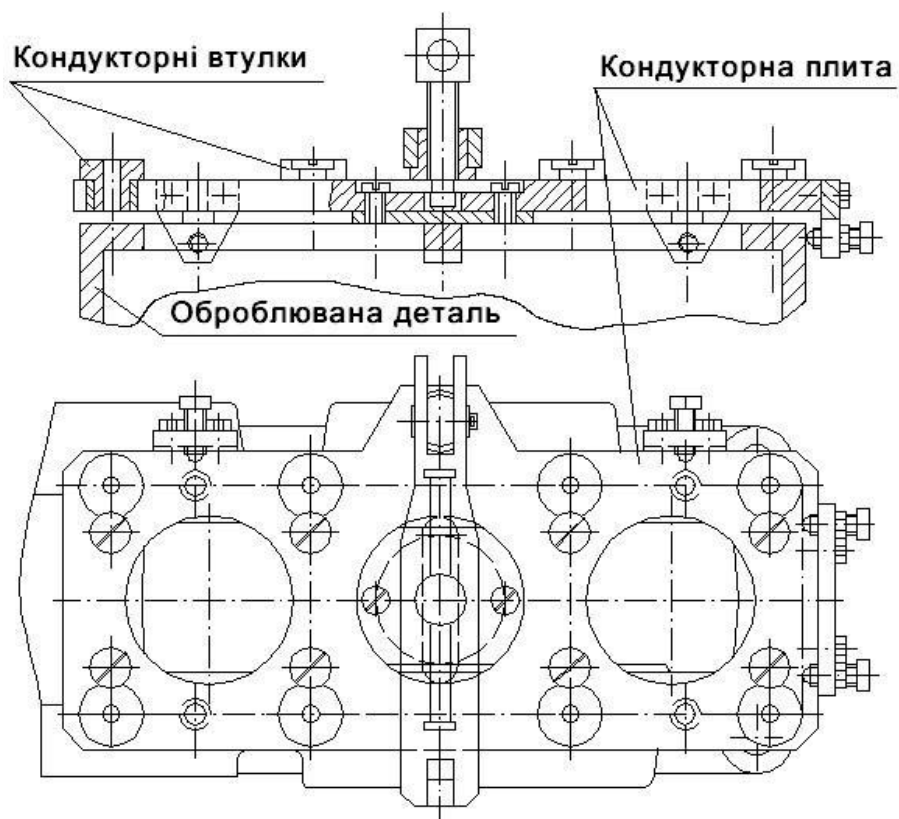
Накладний кондуктор для свердління 8-ми отворів під різьбу М8-7Н
